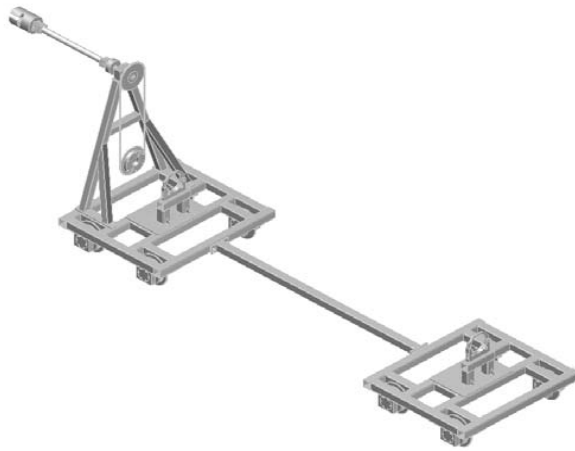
Тележки с приспособлением для вращения оправки в печи
